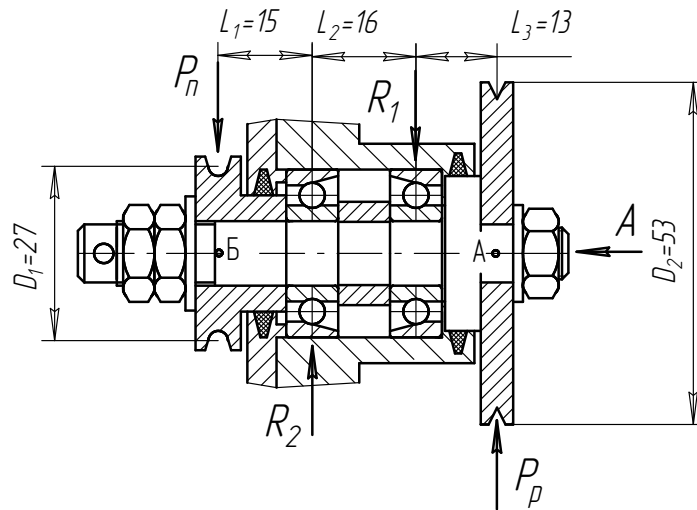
Розрахункова схема для вибору радіально-упорних підшипників інструментальної головки.
